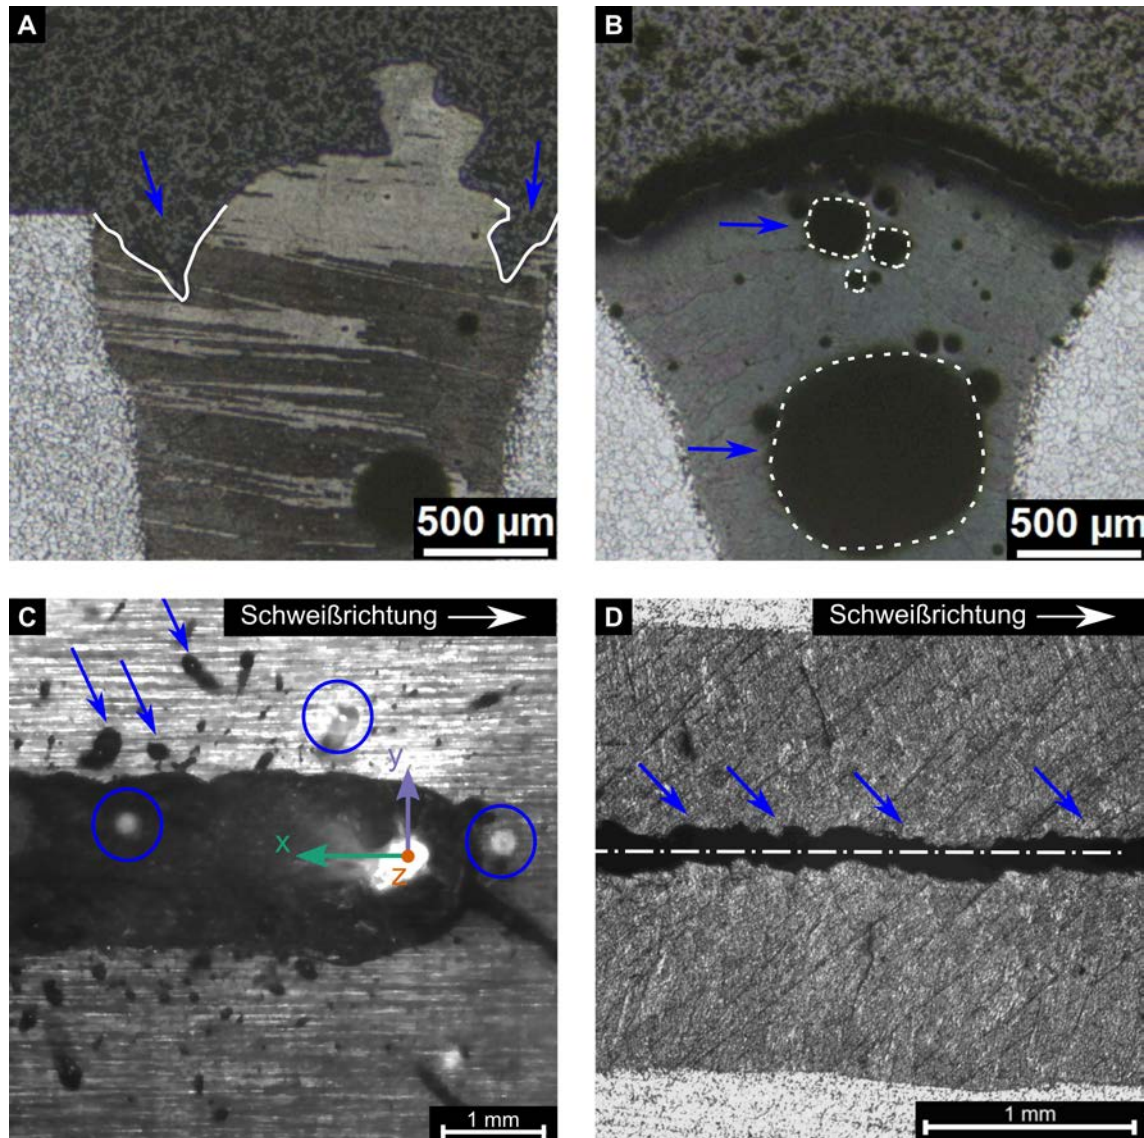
Gängige Fehler im Laserstrahlschweißen. (A) Schlibbild mit Randkerbe, (B) Schlibbild mit Poren, (C) in-situ Hochgeschwindigkeitsaufnahme mit Spritzern, (D) Oberflächenparalleler Schlibb mit Heißriss in der Schweißnahtmitte.
